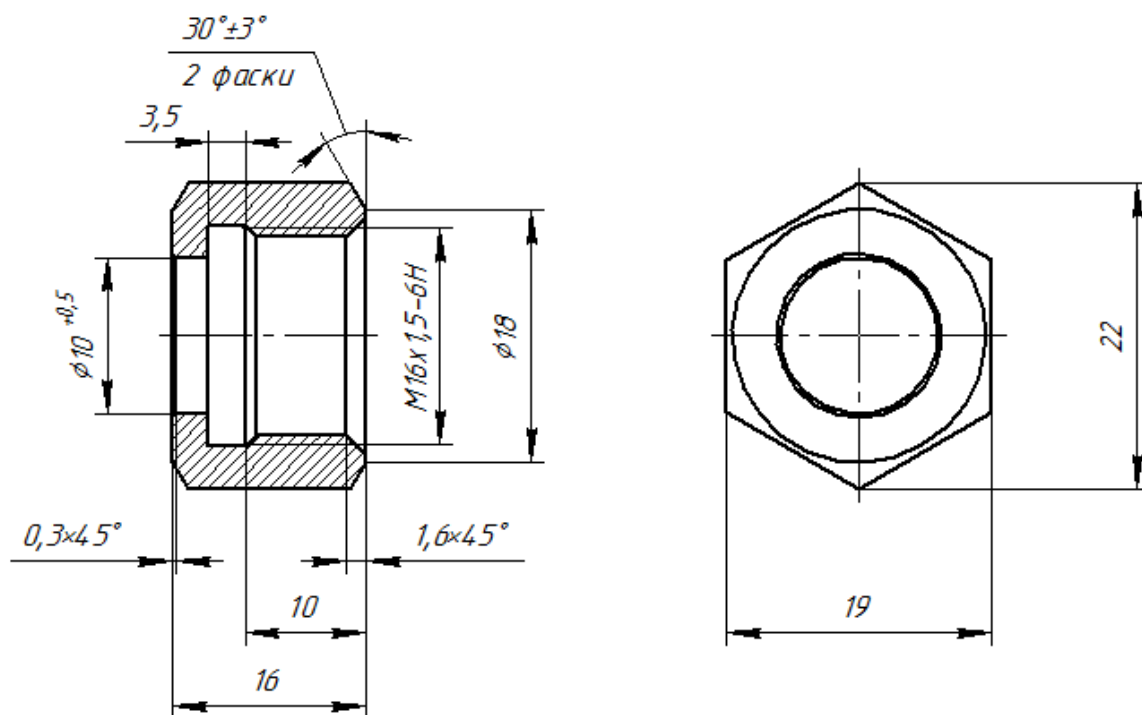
Присоединительные размеры гайки ниппеля ДМ-003-10
